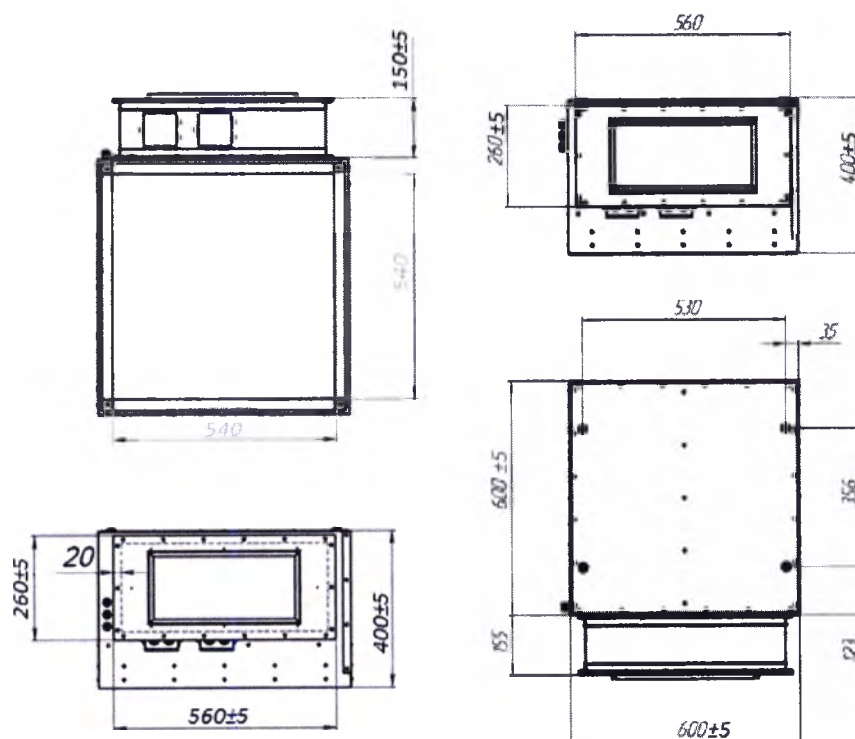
Габаритные размеры и присоединительные размеры моделей «Туон В Lat-M1», «Туон В Lat-M1-S»
